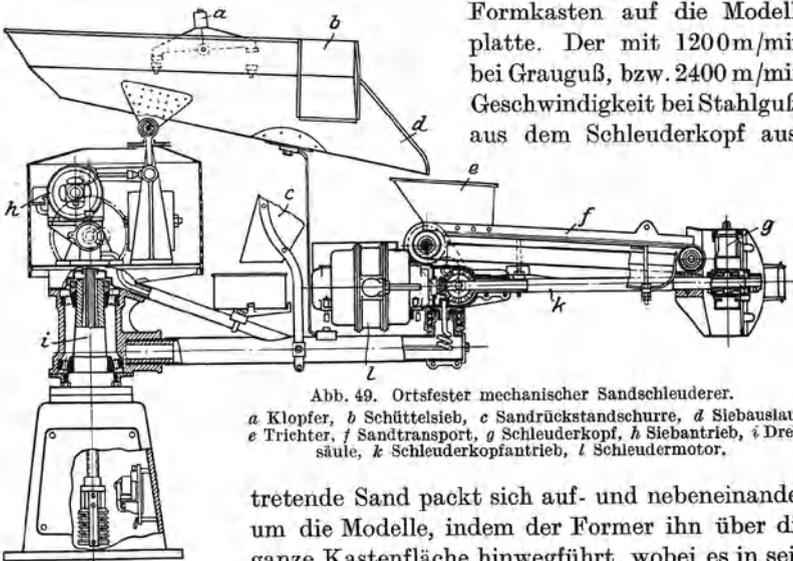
Ortsfester mechanischer Sandschleuderer.
